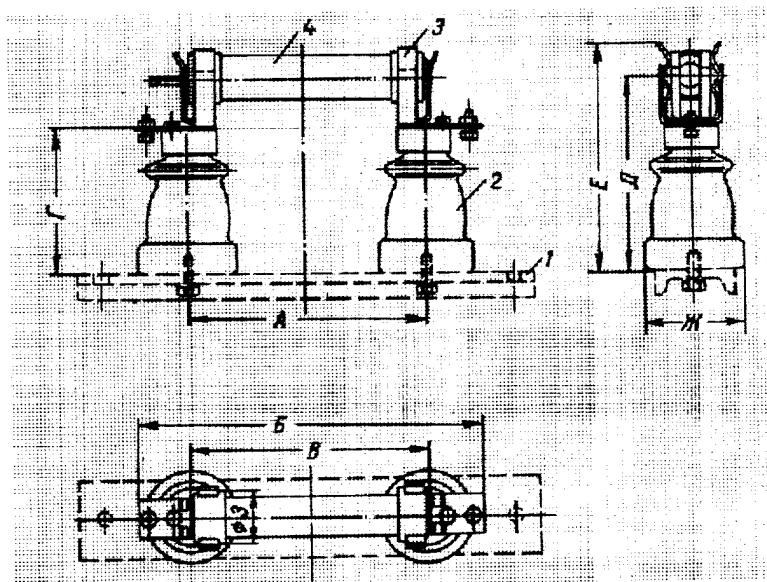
Предохранитель типа ПКТ-6-10-20-35 кв:
